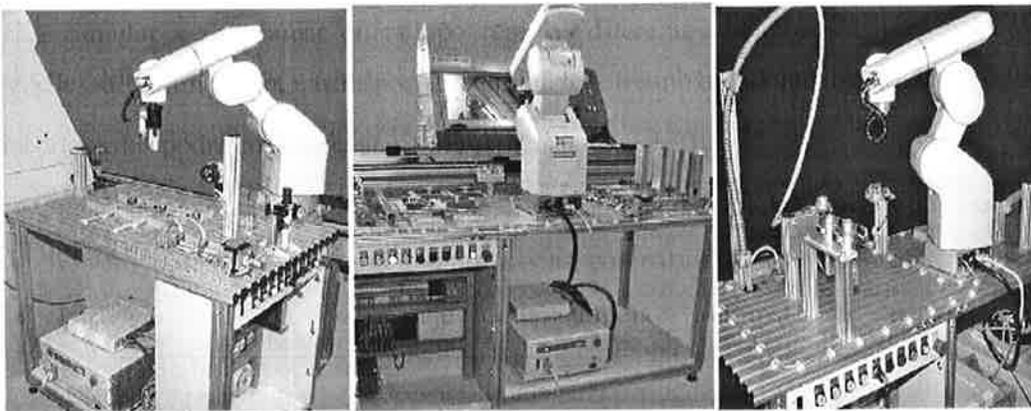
Estaciones de trabajo 1. CNC, 2. Ensamblaje, 3. Soldadura.
